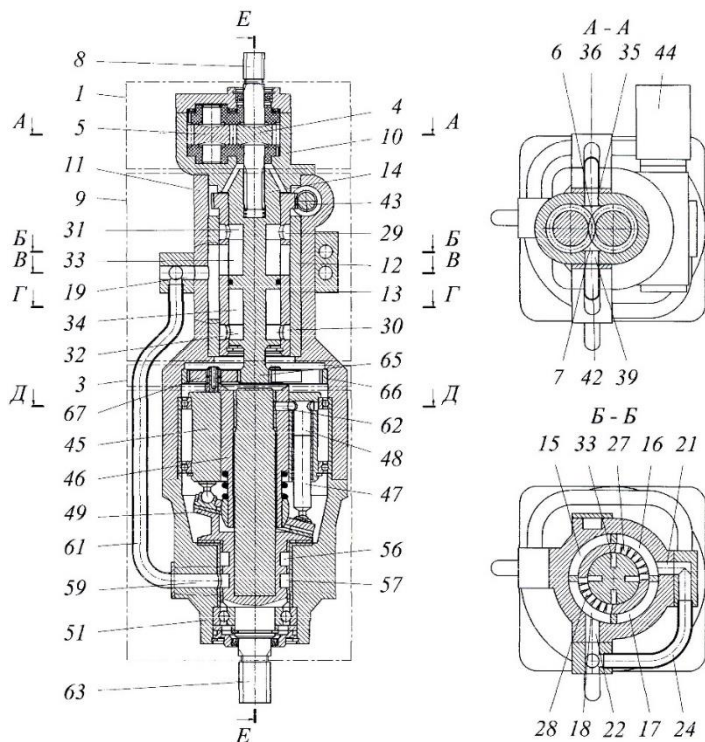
ОГП с планетарным редуктором в линии связи приводного вала и блока цилиндров гидромотора
